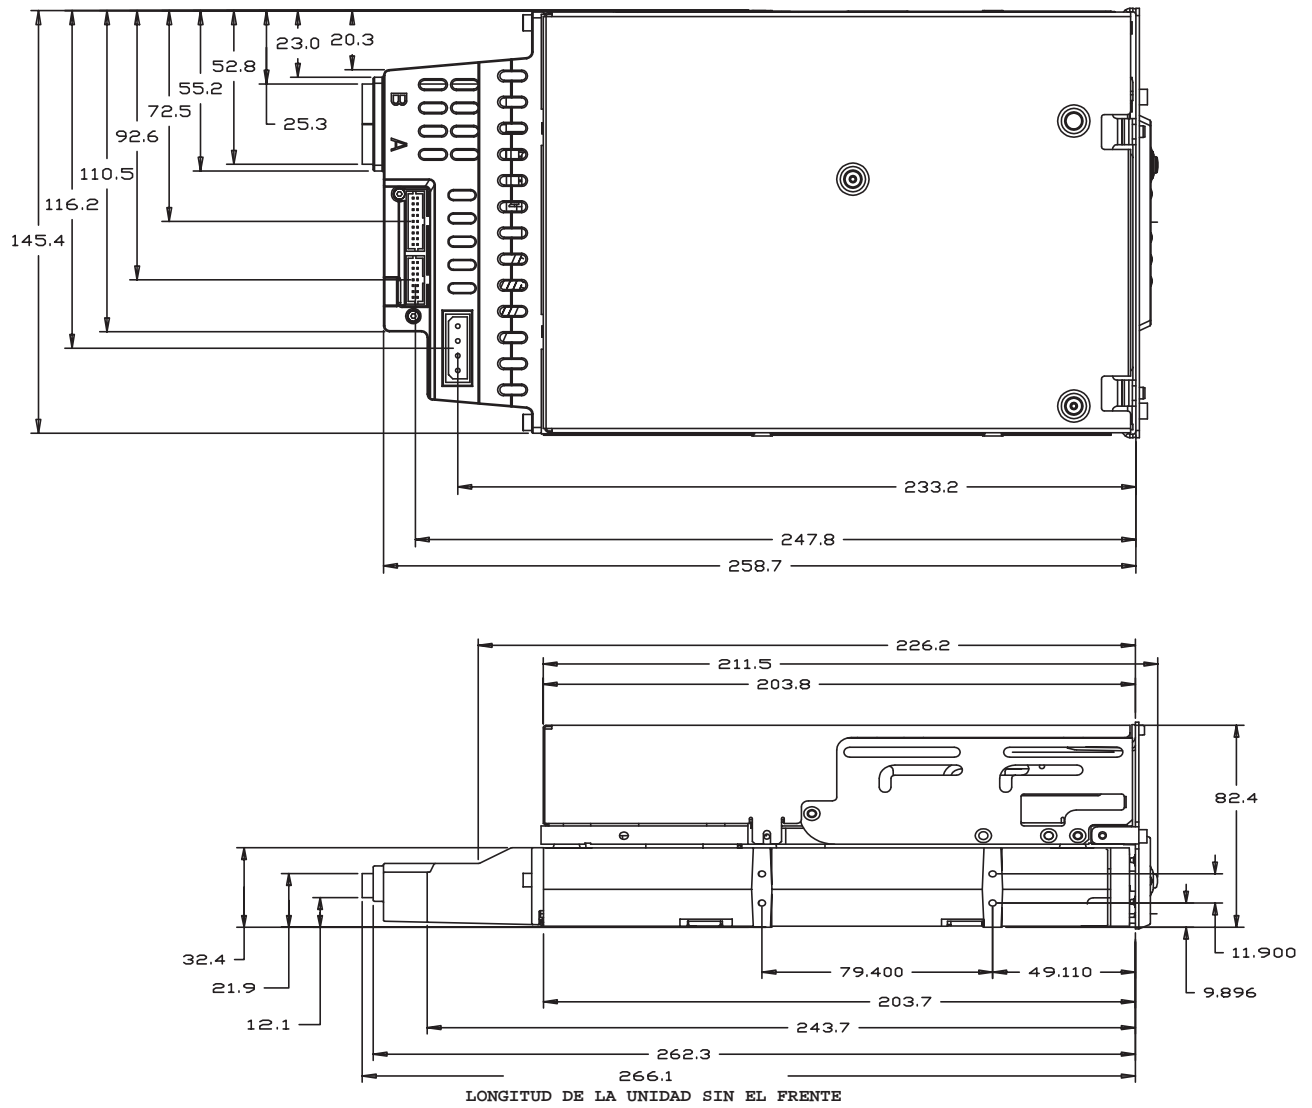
Unidad interna Viper Fibre Channel: dimensiones
